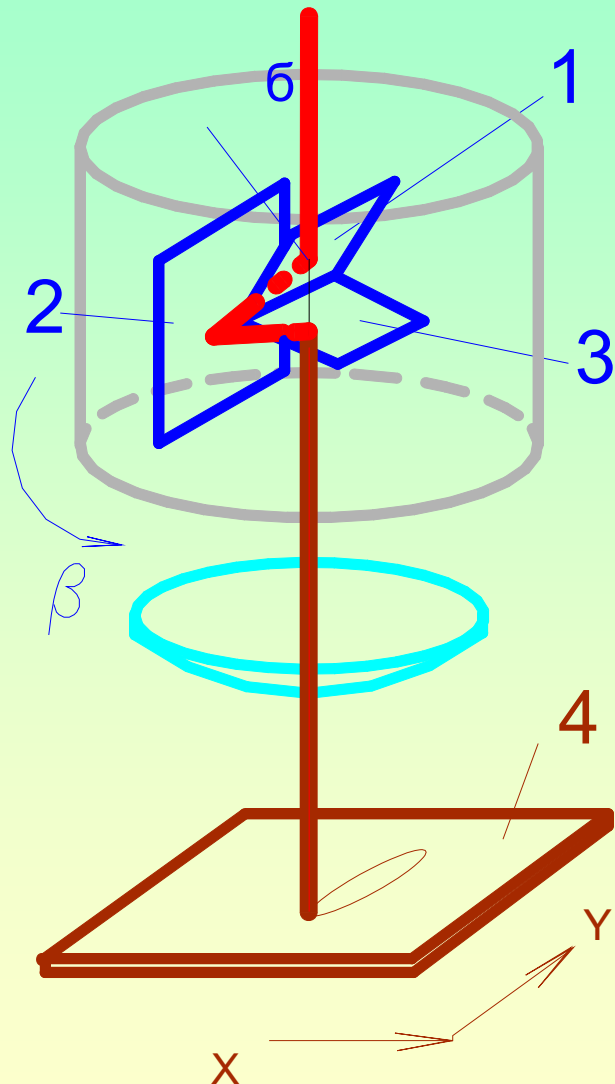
Пристрій для лазерної обробки пазів складної поперечної форми
